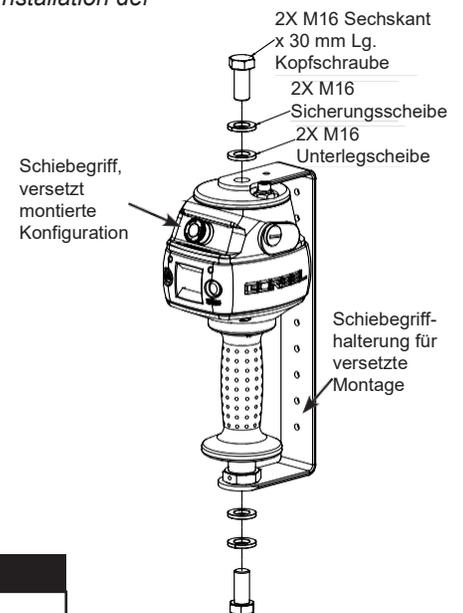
B3. Versetzt montierter Schiebegriff, Explosionszeichnung
